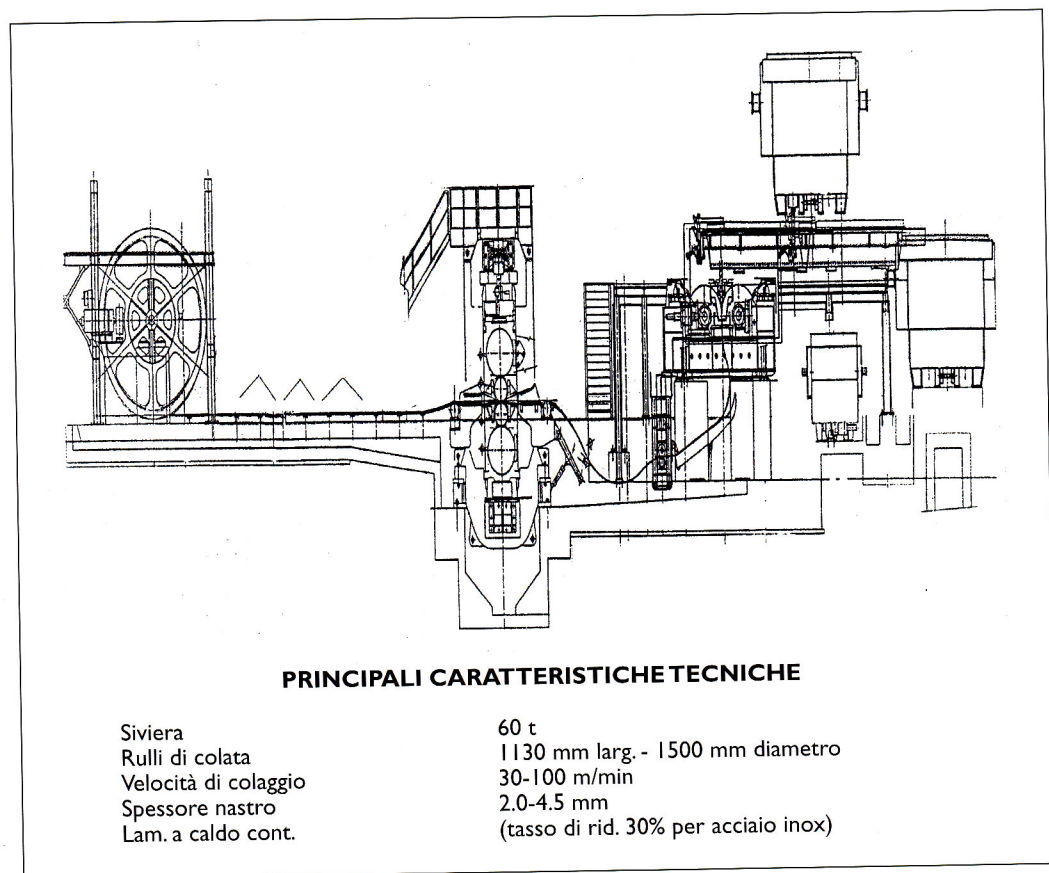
Progetto EUROSTRIP: layout dell'impianto pilota di strip casting di Terni.
